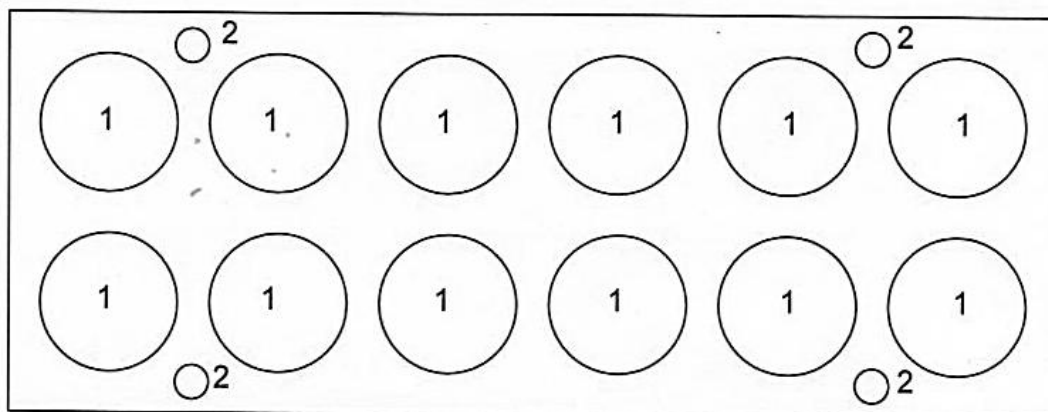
Схема расположения гидроцилиндров: 1 - Главные цилиндры, 2 - цилиндры обратного хода
